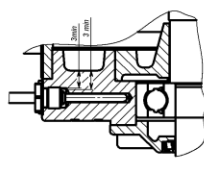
Чертеж взрывозащиты двигателей ВА (Б), 1PBA200,225; BRA(Б), 1PBA200,225,250
